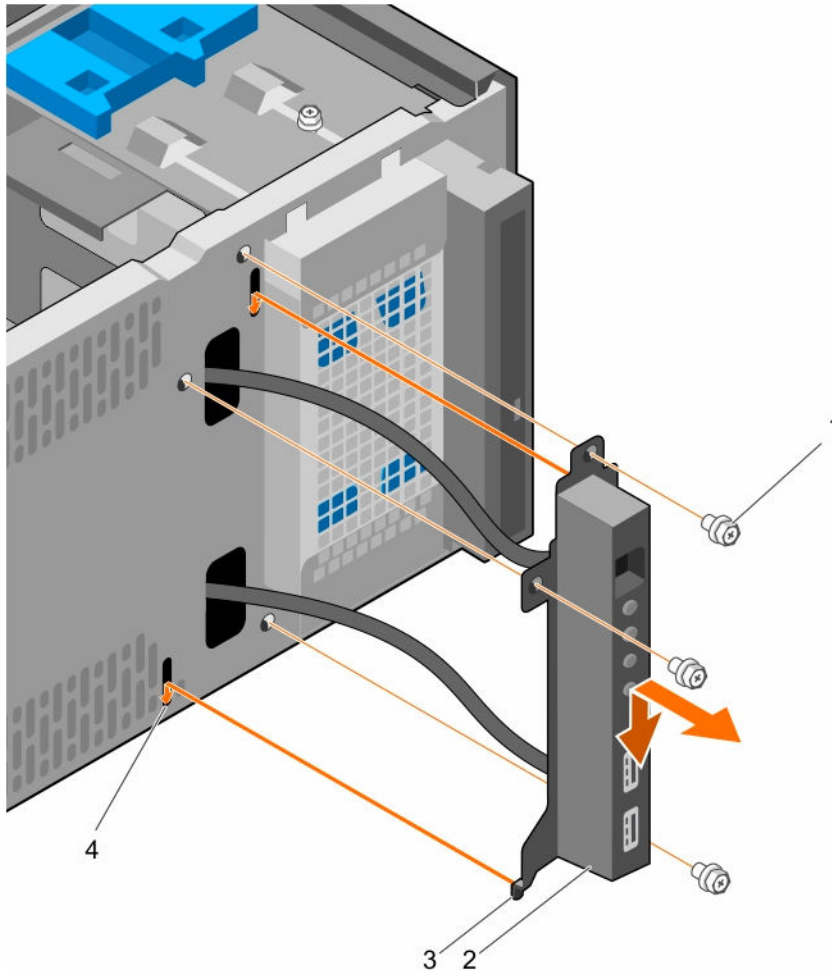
Entfernen und Installieren der Bedienfeldbaugruppe
